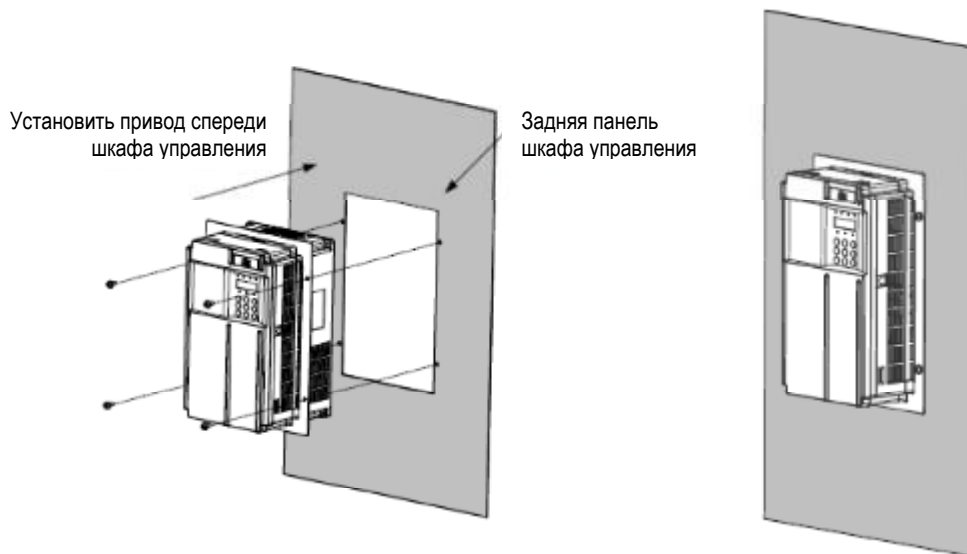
Встраиваемый монтаж для MD290 (пластмассовый корпус)
